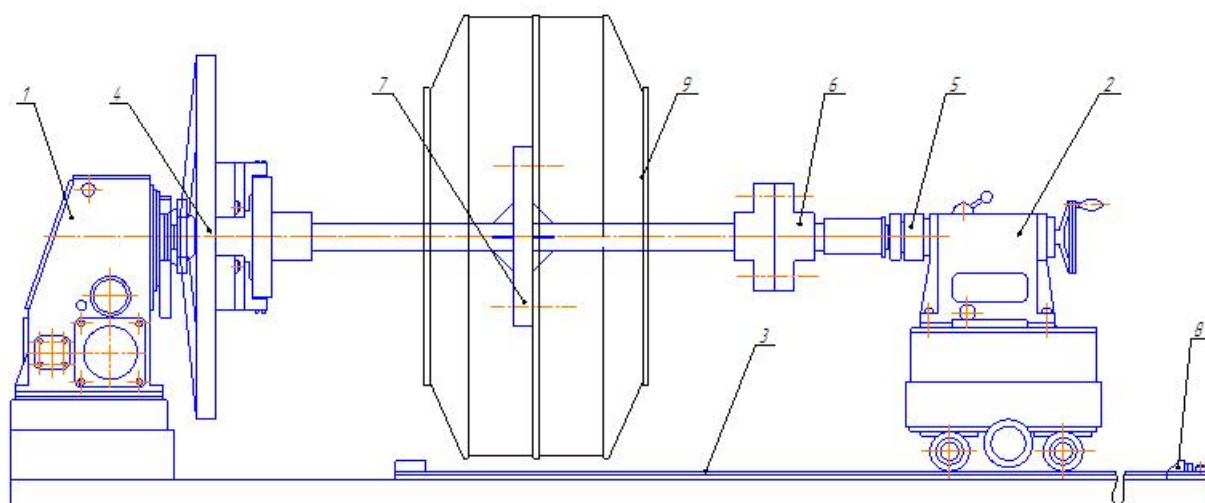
Установка для сварки и наплавки
